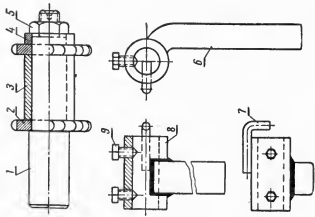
Устройство для одновременного фрезерования двух пазов на пальце рессоры автомобиля ГАЗ-51:
